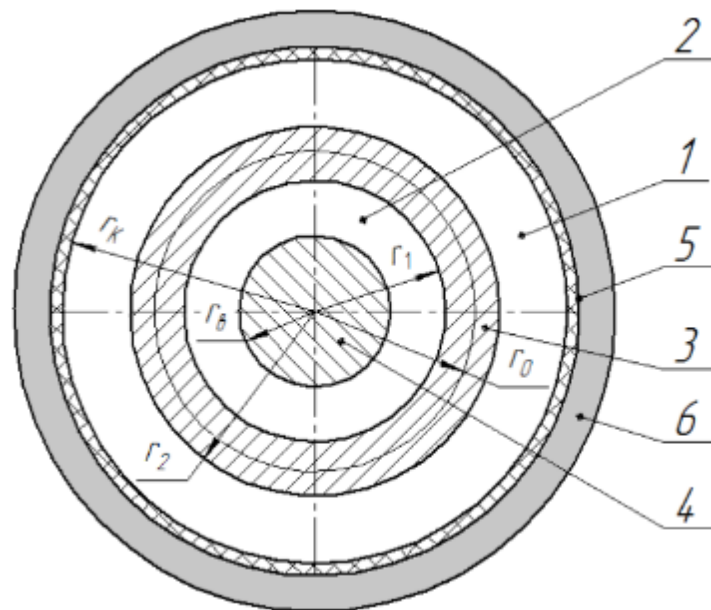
Схема поперечного перерізу осердя індукційного нагрівача рідини: 1 – зовнішній кільцевий зазор; 2 - внутрішній кільцевий зазор; 3 – труба - сердечник нагрівача; 4 – витискувач; 5 – корпус; 6 – індуктор
